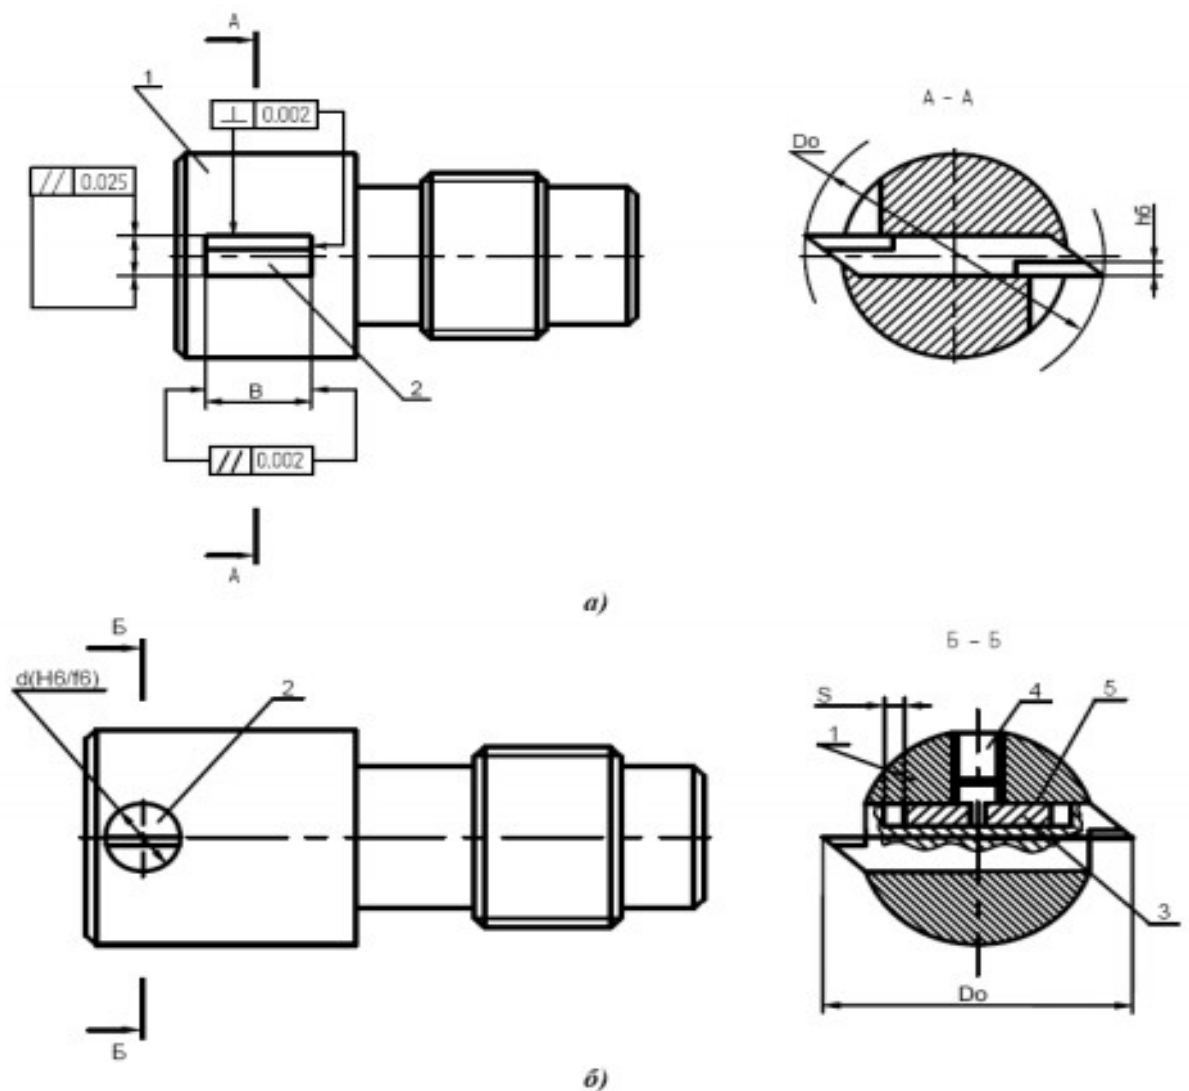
Головки для чистового розточування глибоких отворів:
